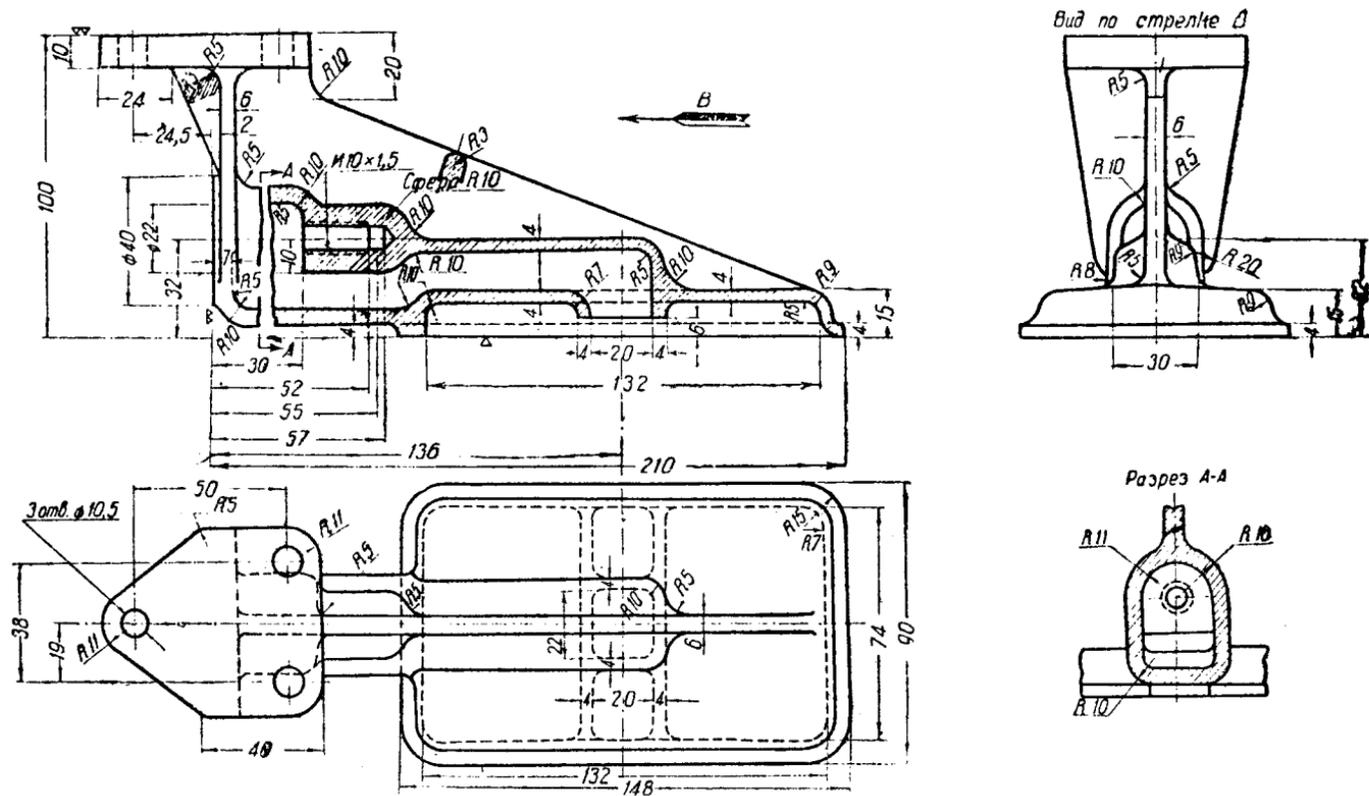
Дет. № 0993. Корпус маслоприёмника переднего
